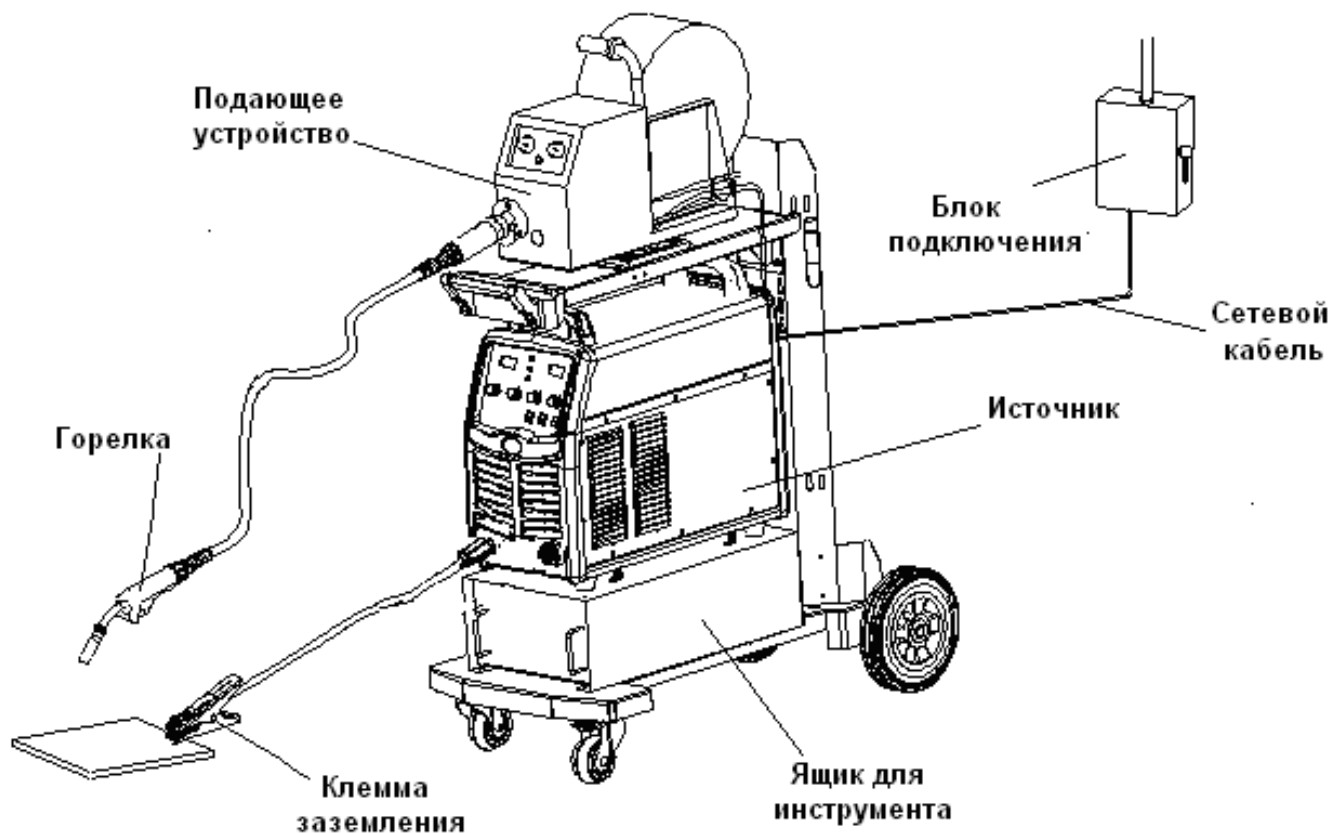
Схема подключения оборудования для механизированной (FCAW) сварки самозащитной порошковой проволокой.
